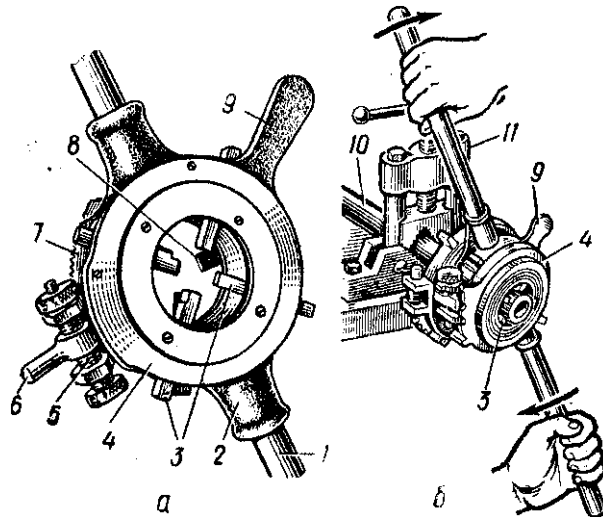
Трубний клуп з розсувними плашками для нарізування різьб діаметром від 1/2 до 3".
